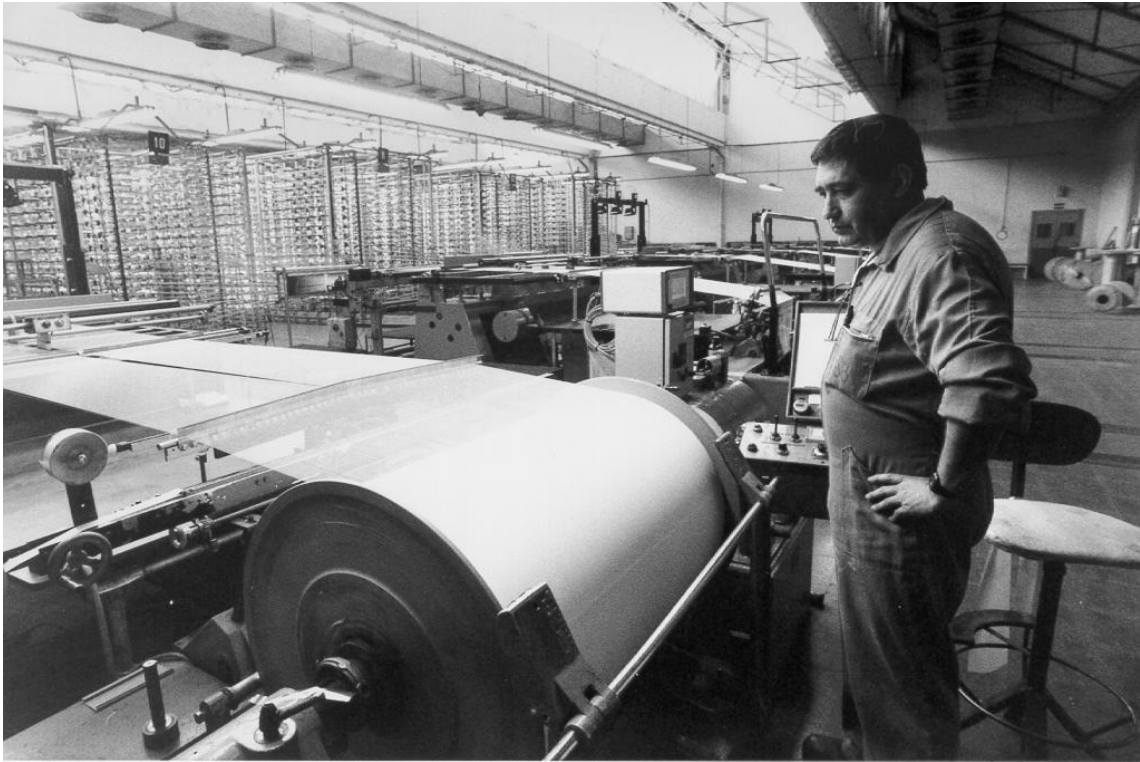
URDIDO. Primer plano del plegador y la zona de trabajo.
